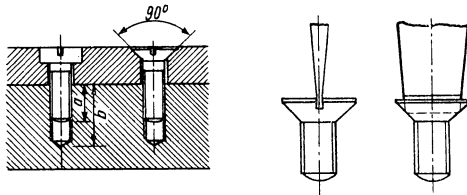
Ausführung versenkter Schraubverbindungen (links); so muß der Schraubenzieher passen, damit der Schraubenkopf nicht beschädigt wird (rechts)
